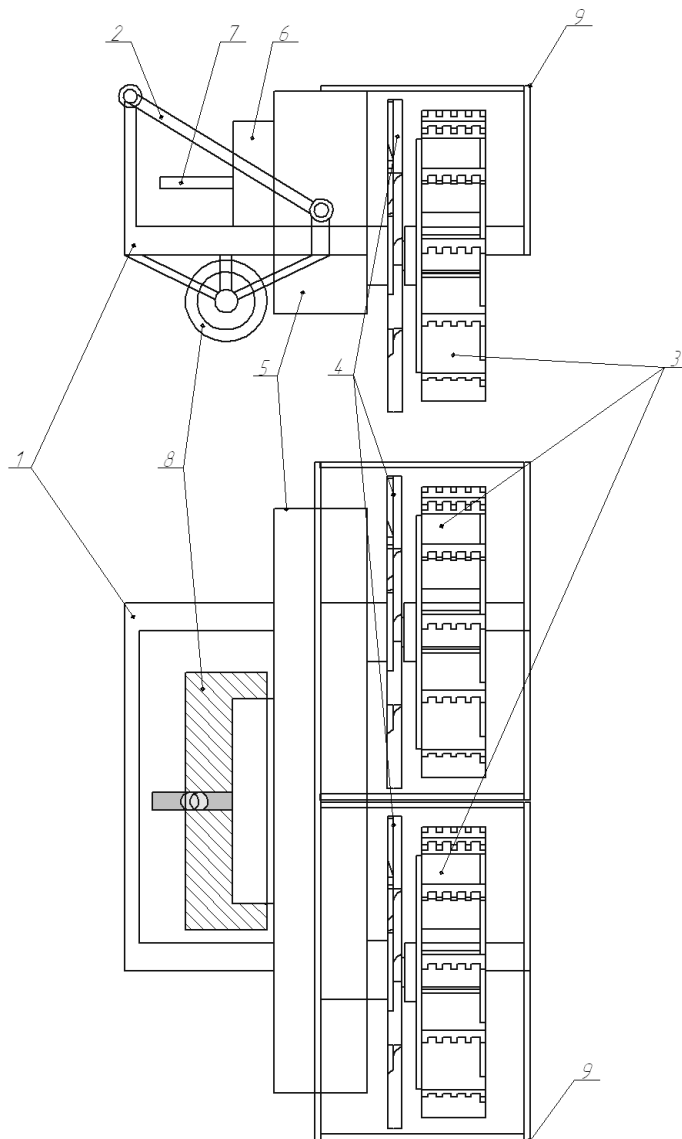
Схема пожежного ґрунтомета: 1 – несуча рама; 2 – навісний пристрій з гідроциліндром підйому та опускання несучої рами; 3 – роторні метачі ґрунту; 4 – роторні фрези розпушувачі ґрунту; 5 – розподільний редуктор; 6 – запобіжна муфта; 7 – карданний вал; 8 – опорні катки; 9 – направляючі кожухи.
